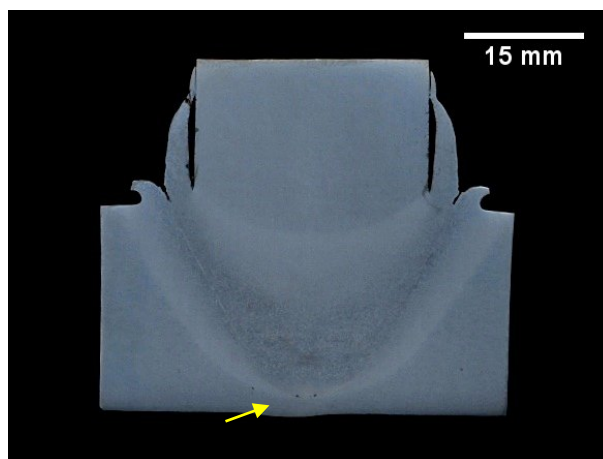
Macrografia da junta soldada de um aço C-Mn.
